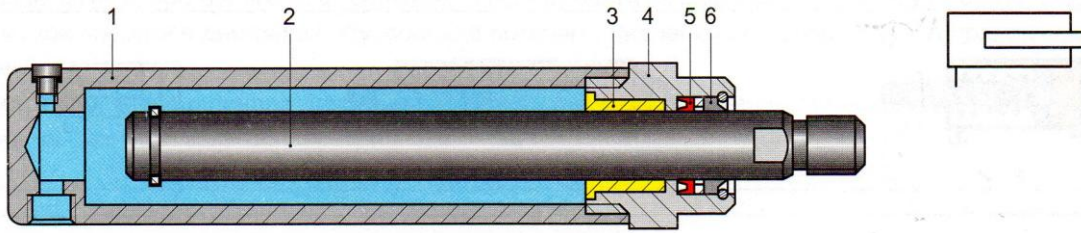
, б. Конструктивная схема плунжерного гидроцилиндра:
